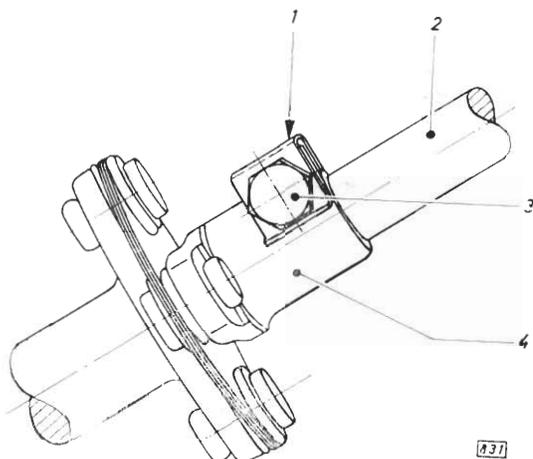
Sicherung der Klemmschraube am Lenkspindelflansch
